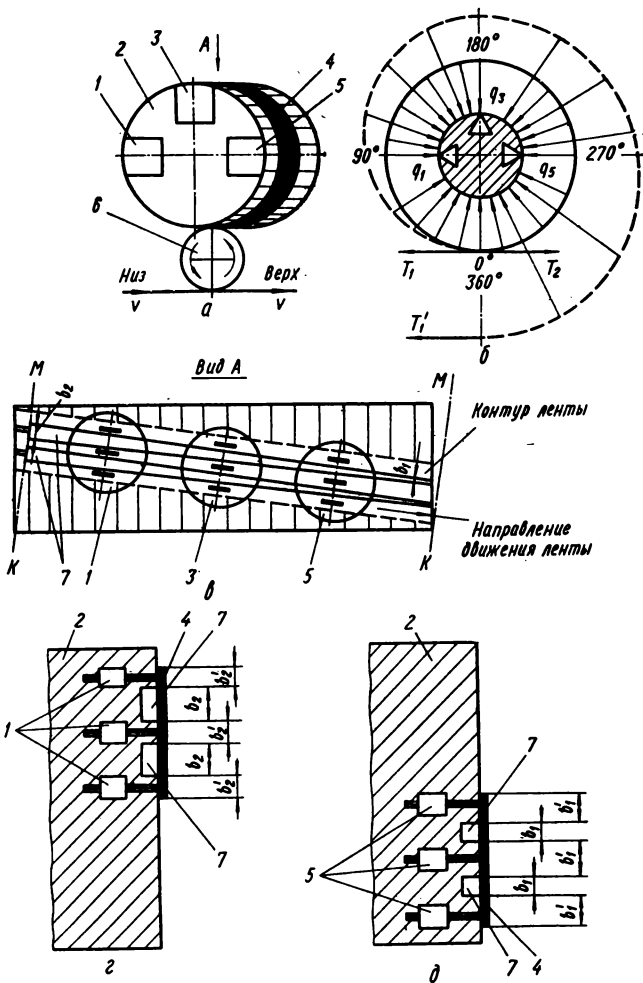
Схемы создания контакта с неподвижными головками в пространственных рабочих зонах, эпюра давлений и развертка барабана.
